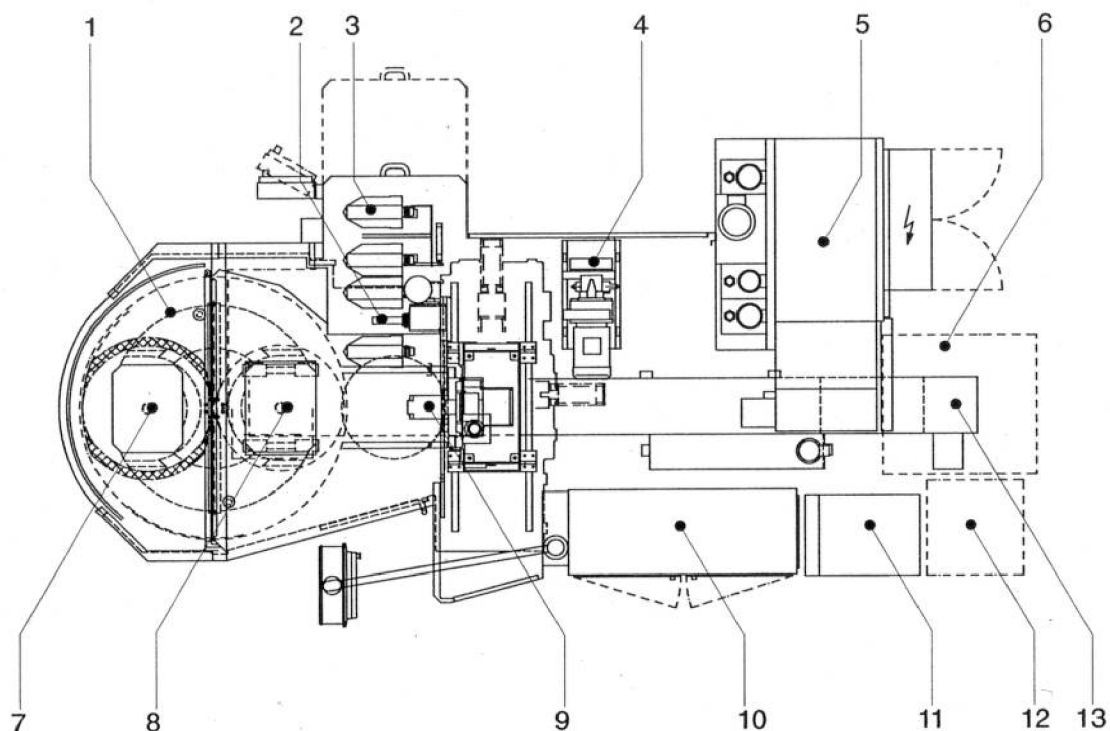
Linka 1, obráběcí centra Heller MC16
